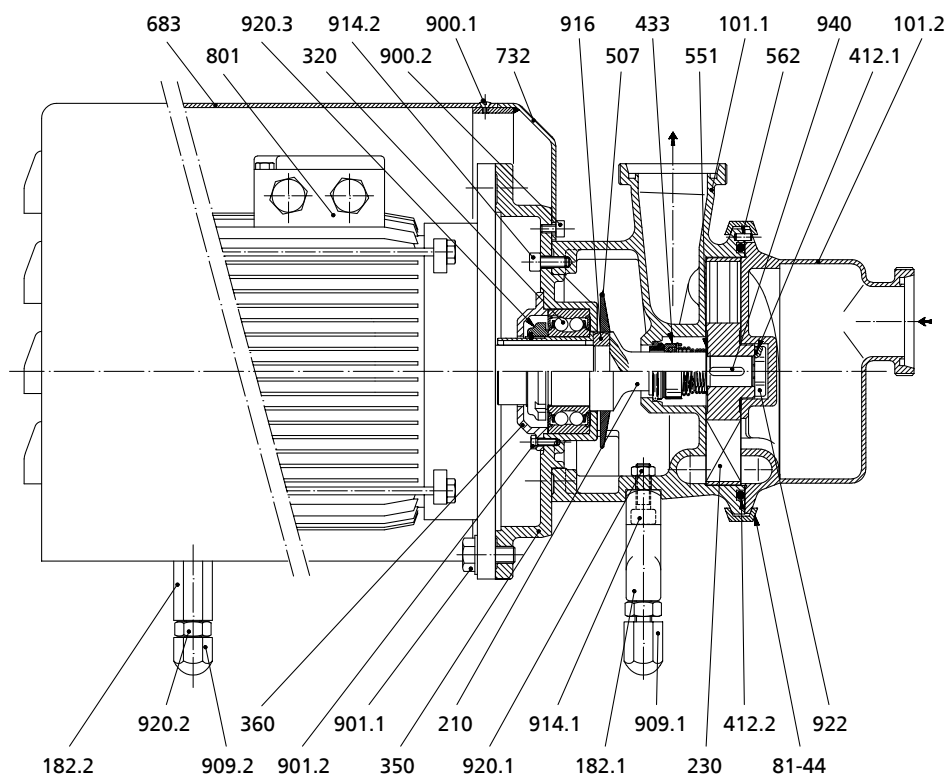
Типоразмер 50-164 / типоразмер двигателя 132
